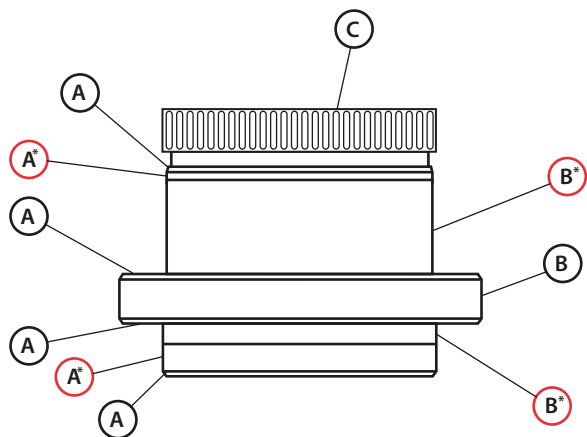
Шлицевая ведущая втулка, важные поверхности
